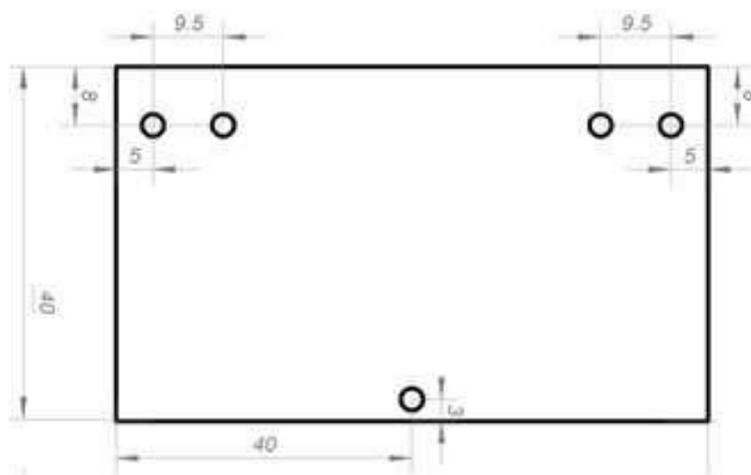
Габаритный чертеж платы Произведите трассировку согласно минимальным допускам:
